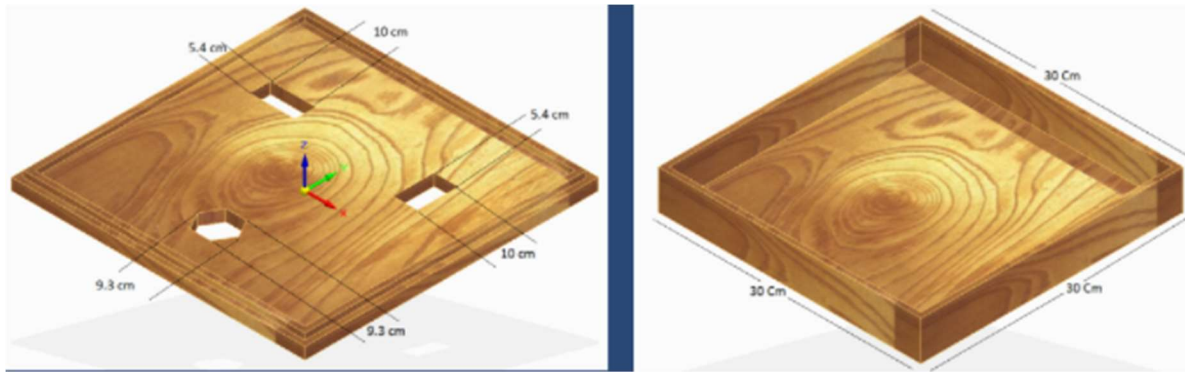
Diseño de módulo como apoyo para la realización el ensamble físico, fuente autores.
